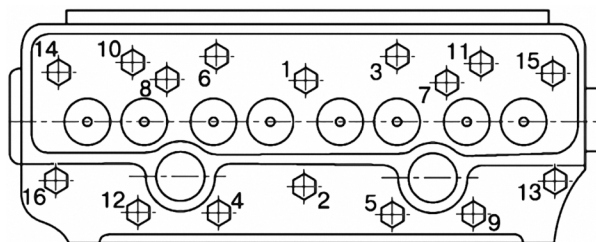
Схема последовательности затяжки болтов крепления головки цилиндров двигателя Д-245
